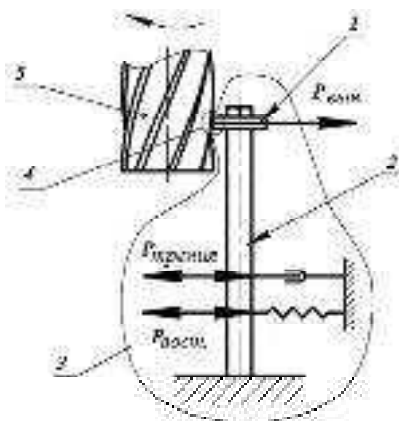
Схема стэнда для вивчення процесу фрезерування деталей з різною жорсткістю: 1 – оброблюваний образец; 2 – пружна пластина; 3 – пружна система деталь – приспособление; 4 – зона різання; 5 – кінцева фреза
